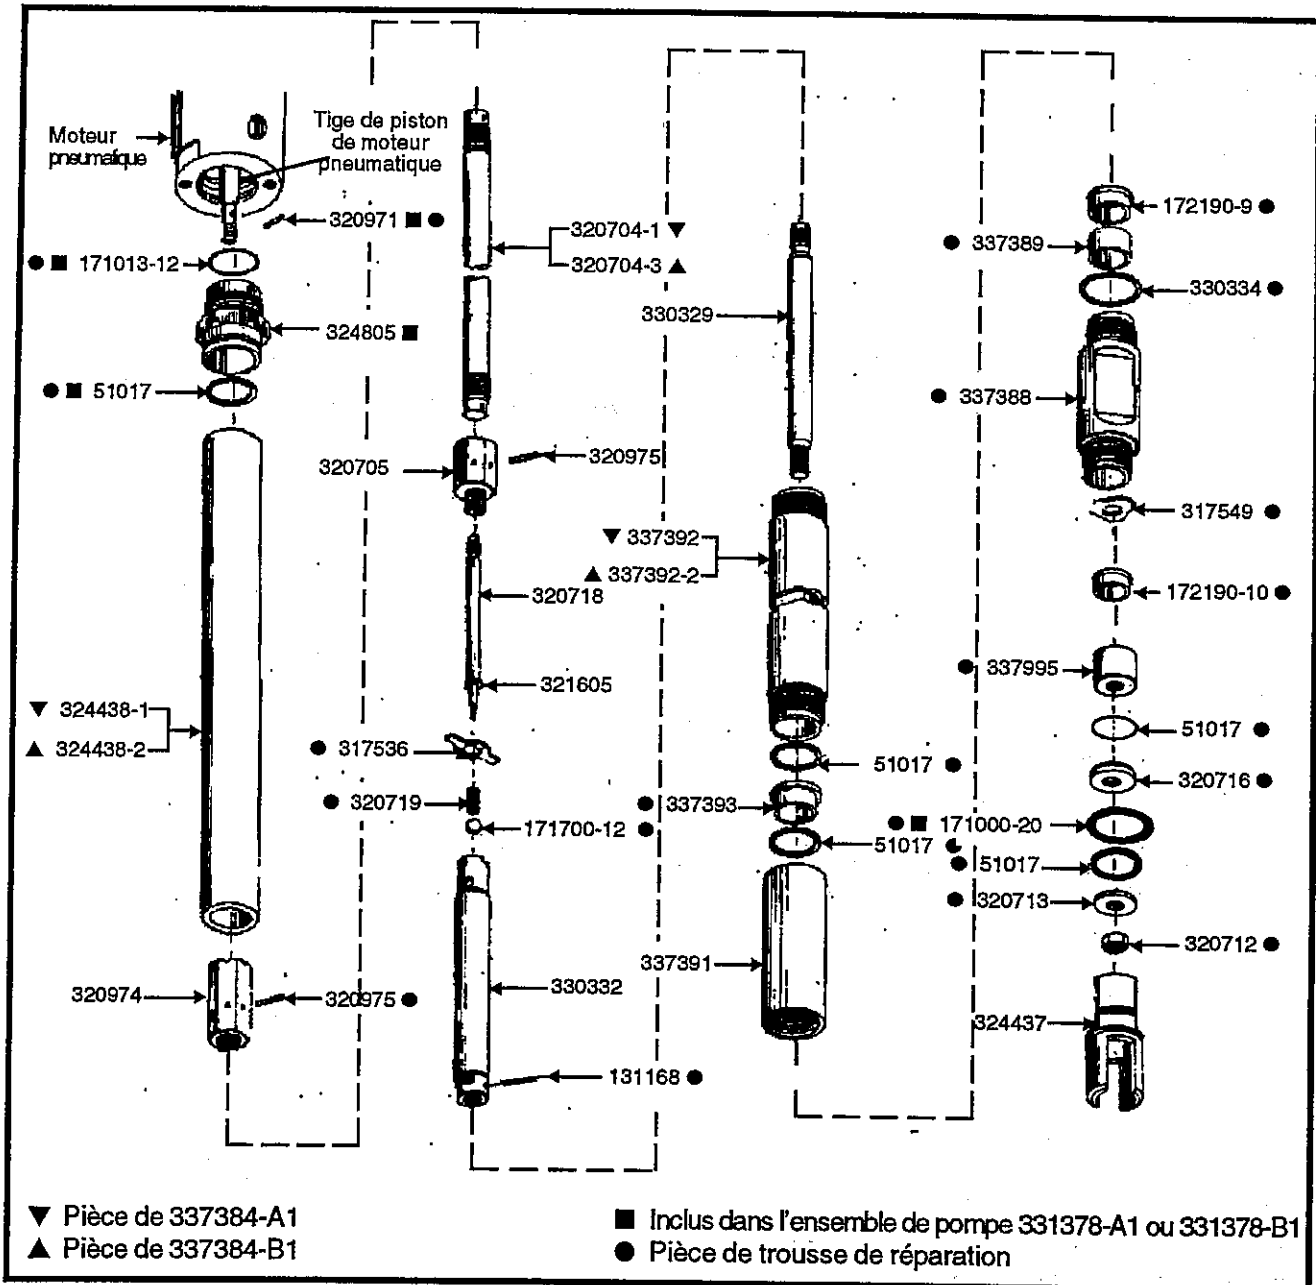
Réassemblage du tube de pompe 337384-A1 ou 337384-B1
